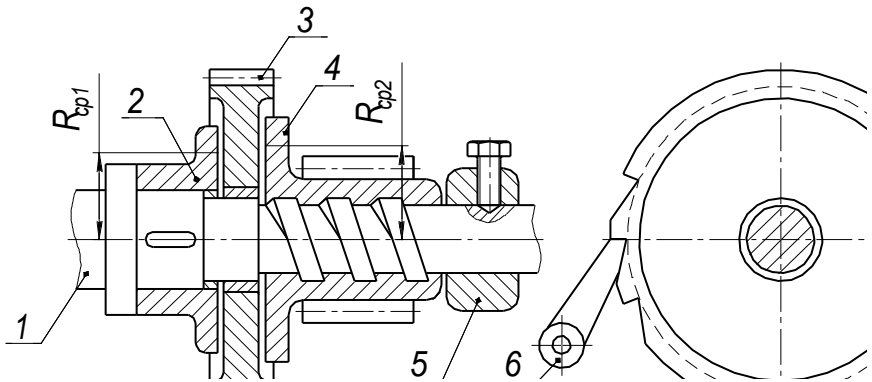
Схема грузоупорного тормоза: 1 – тормозной вал; 2, 4 – тормозные диски; 3 – храповое колесо; 5 – упор; 6 – собачка
